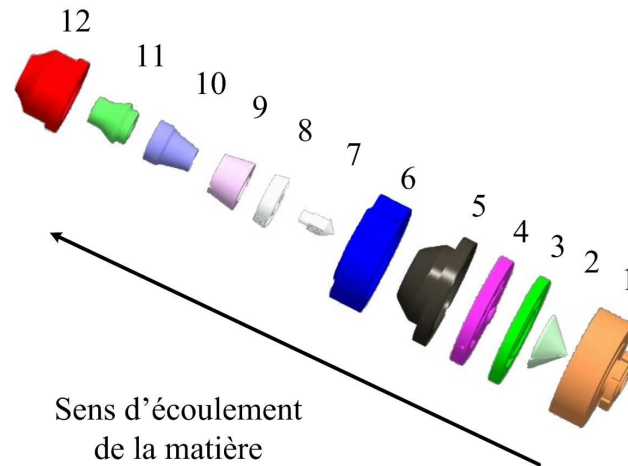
Vue éclatée d'une tête d'extrusion.
